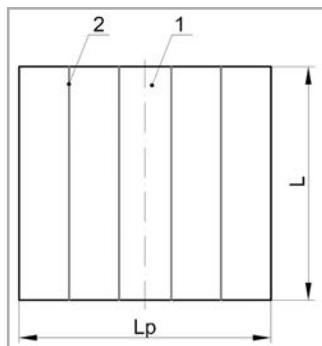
Схема развертки обечайки (листового полотна): 1 – лист; 2 – сварной шов; L – ширина полотна (длина обечайки); Lp – длина полотна (длина развертки обечайки)
